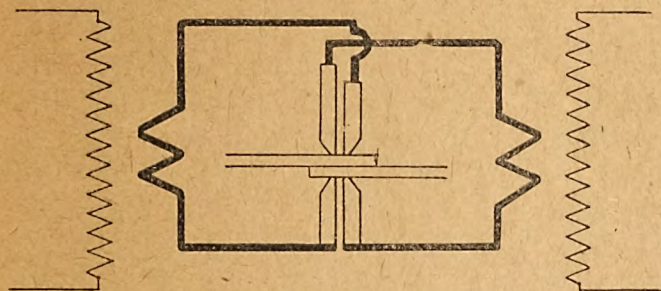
Soudure par recouvrement à 2 secondaires.
